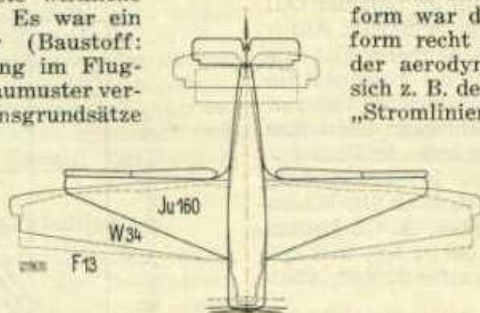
Grundrisse der Baumuster F 13, W 34 und Ju 160, in gleichem Maßstab übereinander gezeichnet.
